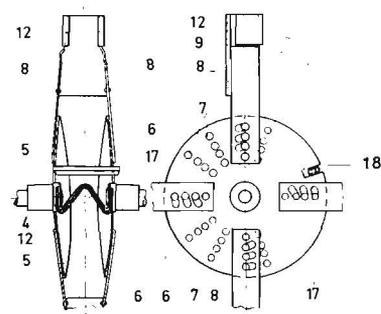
Die Zuführgänge der Maschine nach Bild 5a in größerem Maßstab (links im Schnitt, rechts in Seitenansicht)
